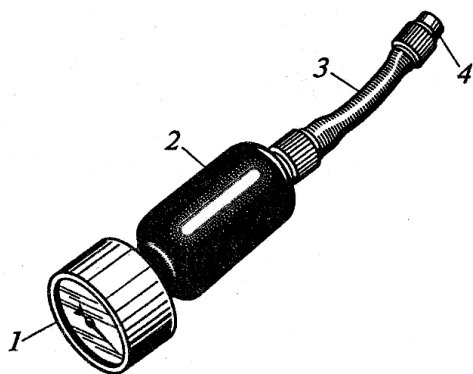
Приспособление КИ-28095 для измерения давления наддувочного воздуха: 1 – манометр; 2 – корпус; 3 – соединительный шланг; 4 – присоединительный штуцер.
